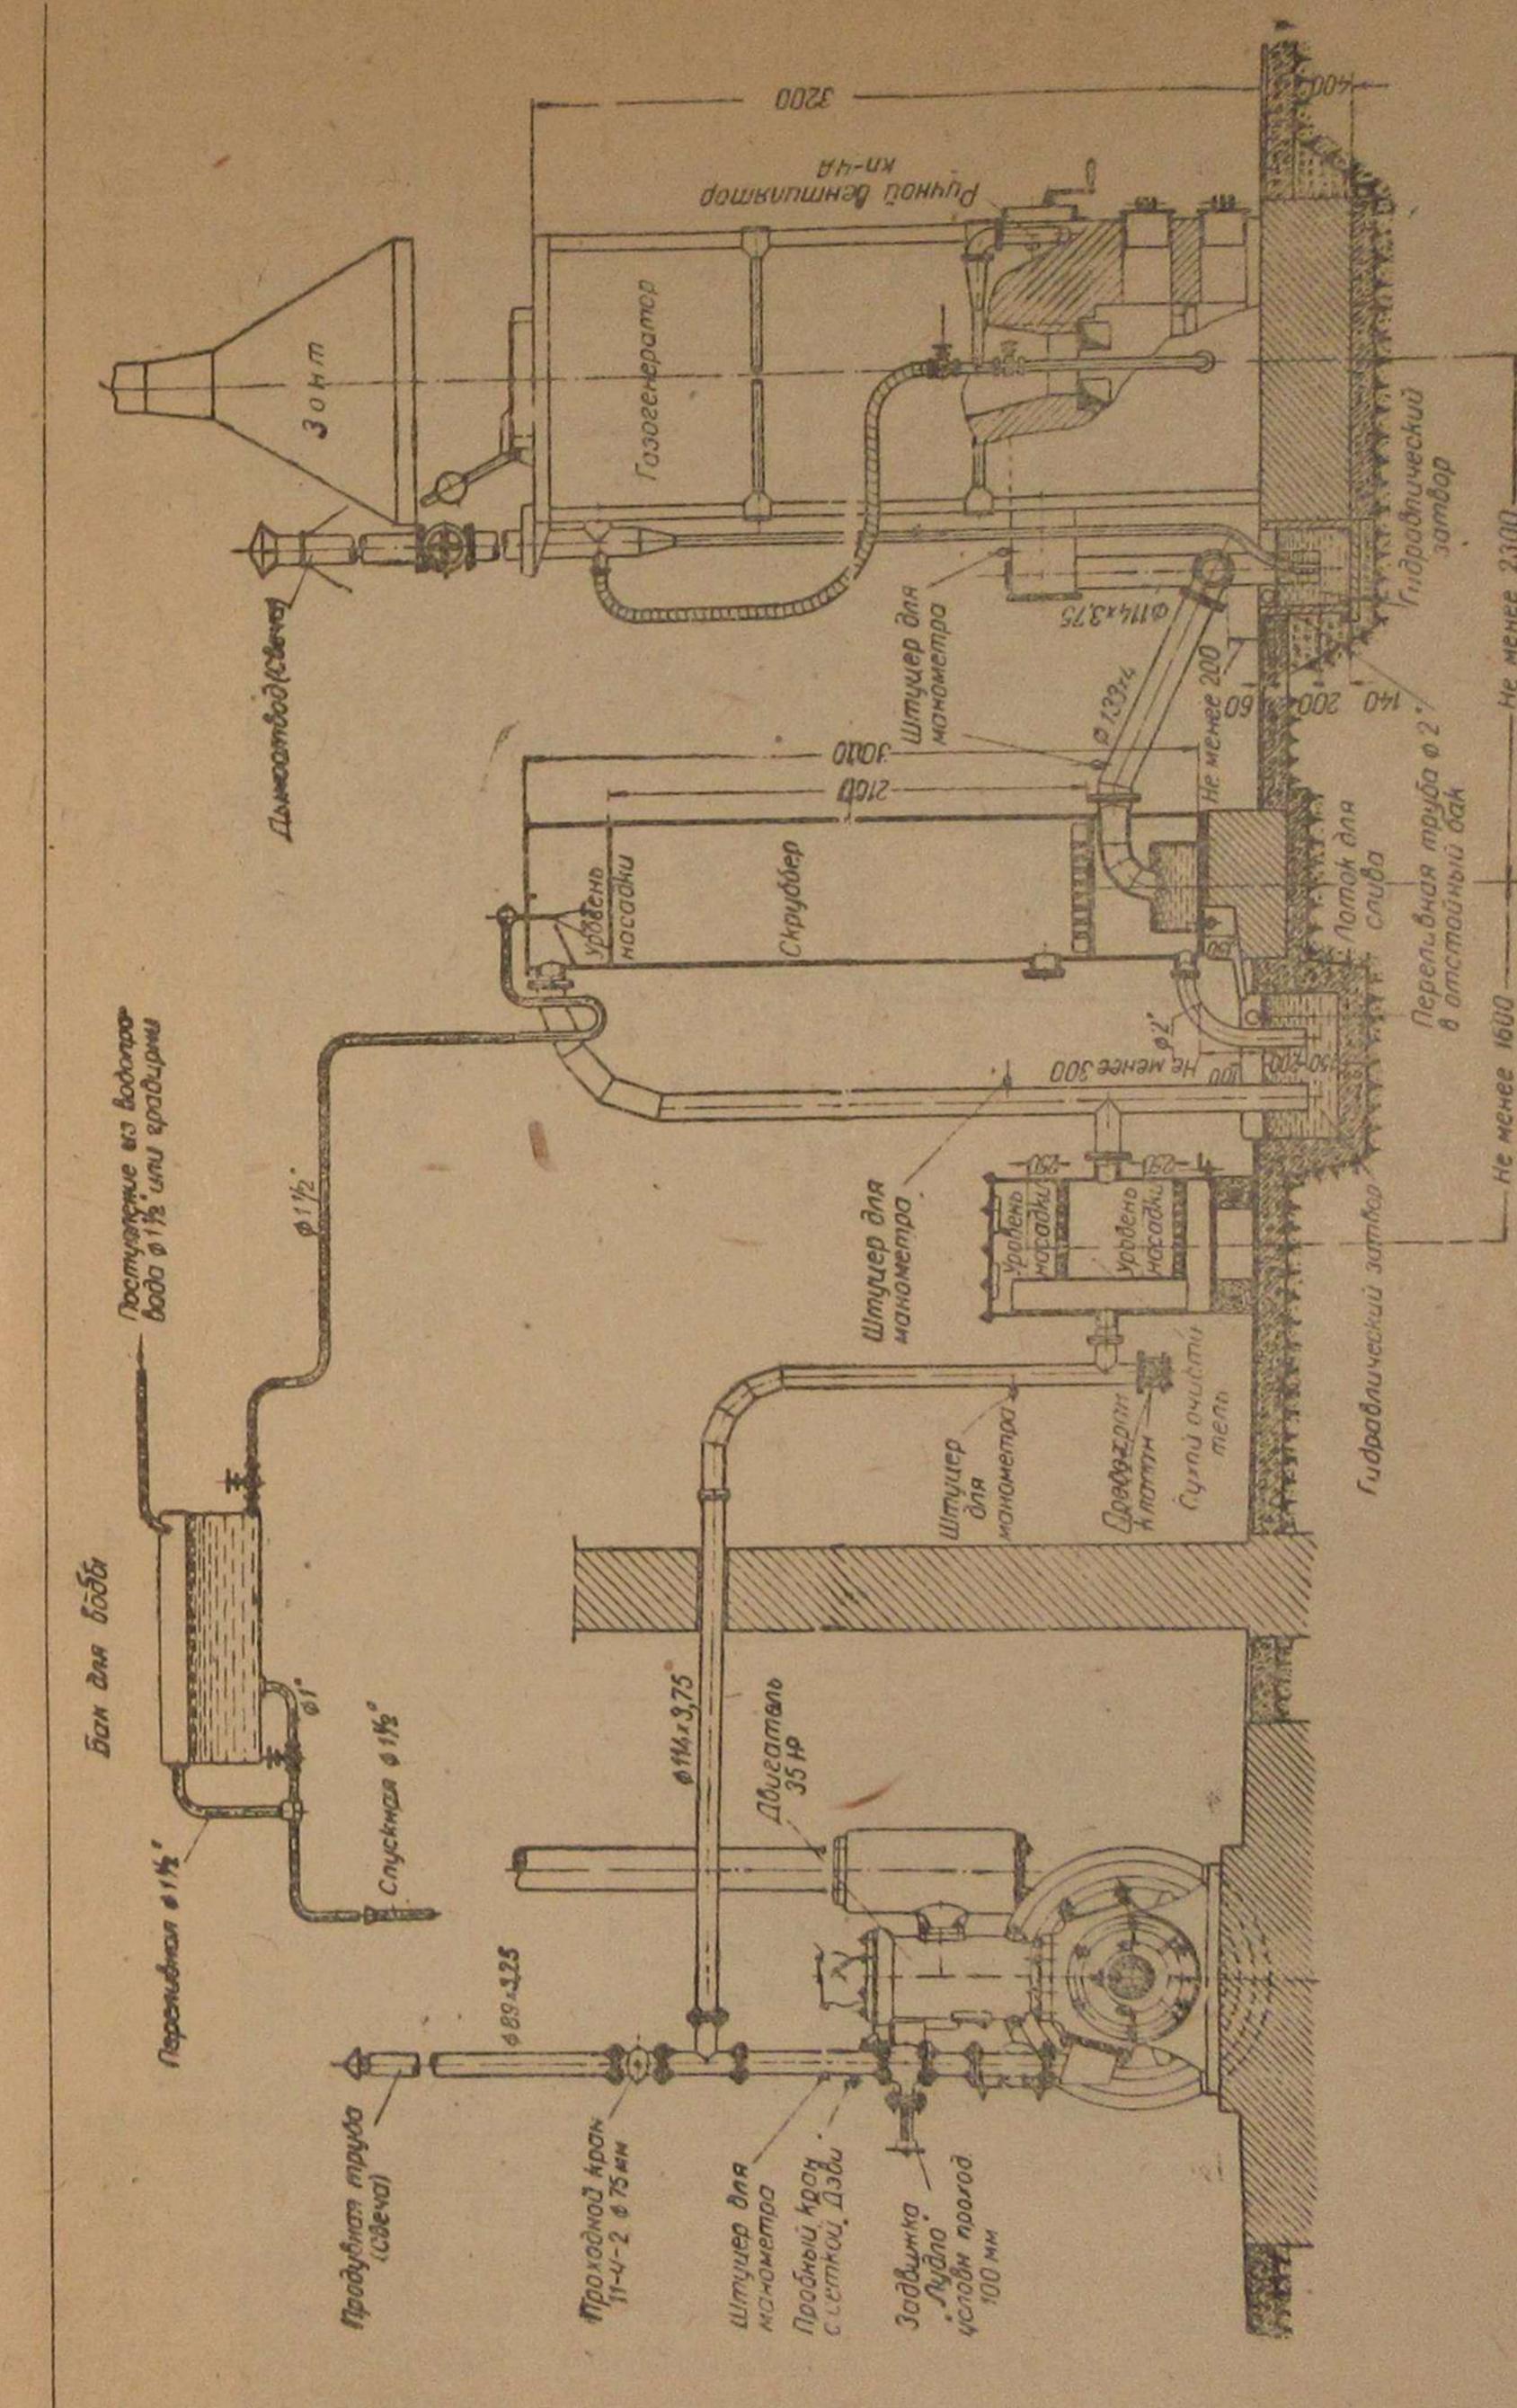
Схема газогенераторной установки для двигателя ДВ-35
